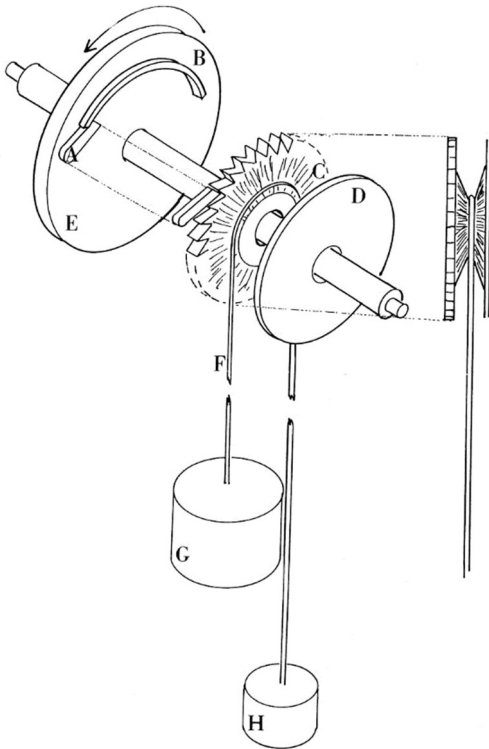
Gewichts Antrieb einer Achttagenuhr (vgl. auch die Detail-Angaben der Zeichnung „Aufzug“)
